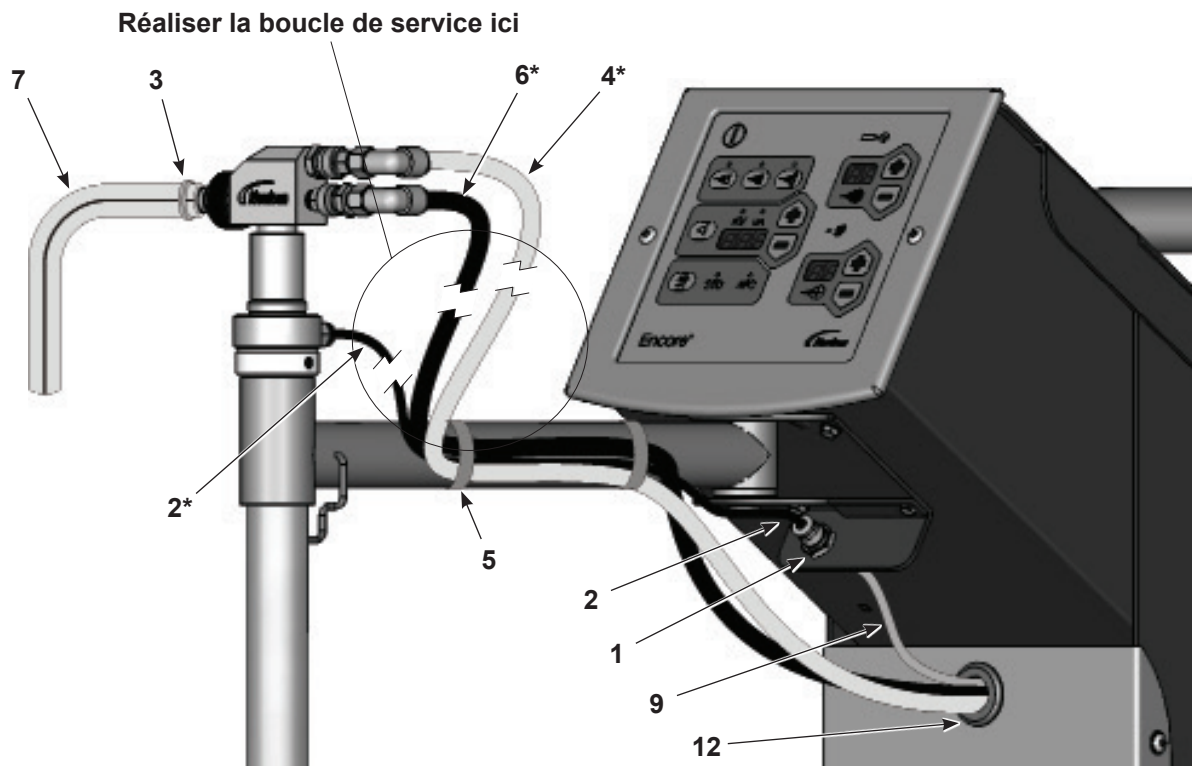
Installation du tube de prélèvement pour pistolet Encore LT et de la pompe
